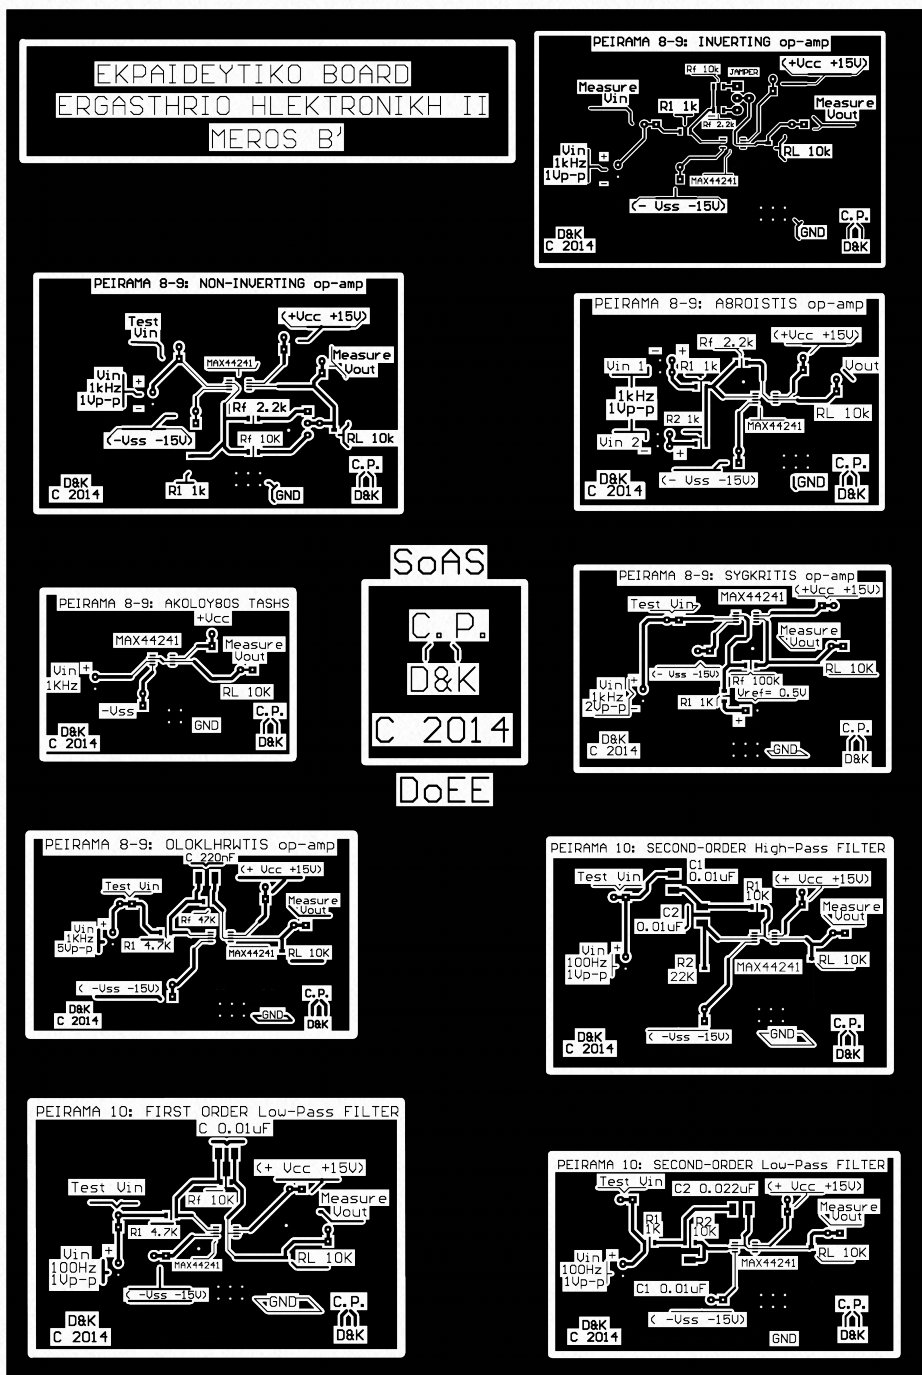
Διαφάνεια Εμφάνιση PCB
